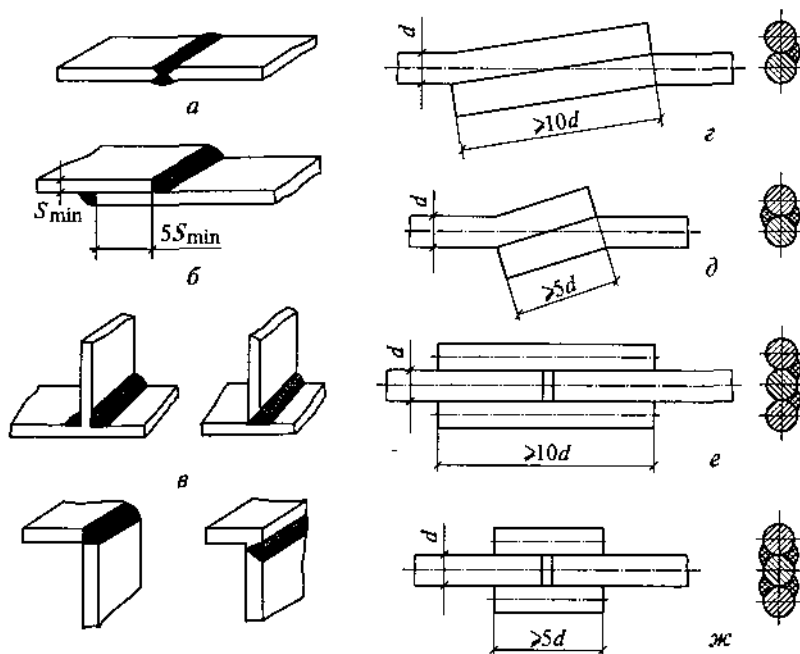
Основные виды сварных соединений и швов:
